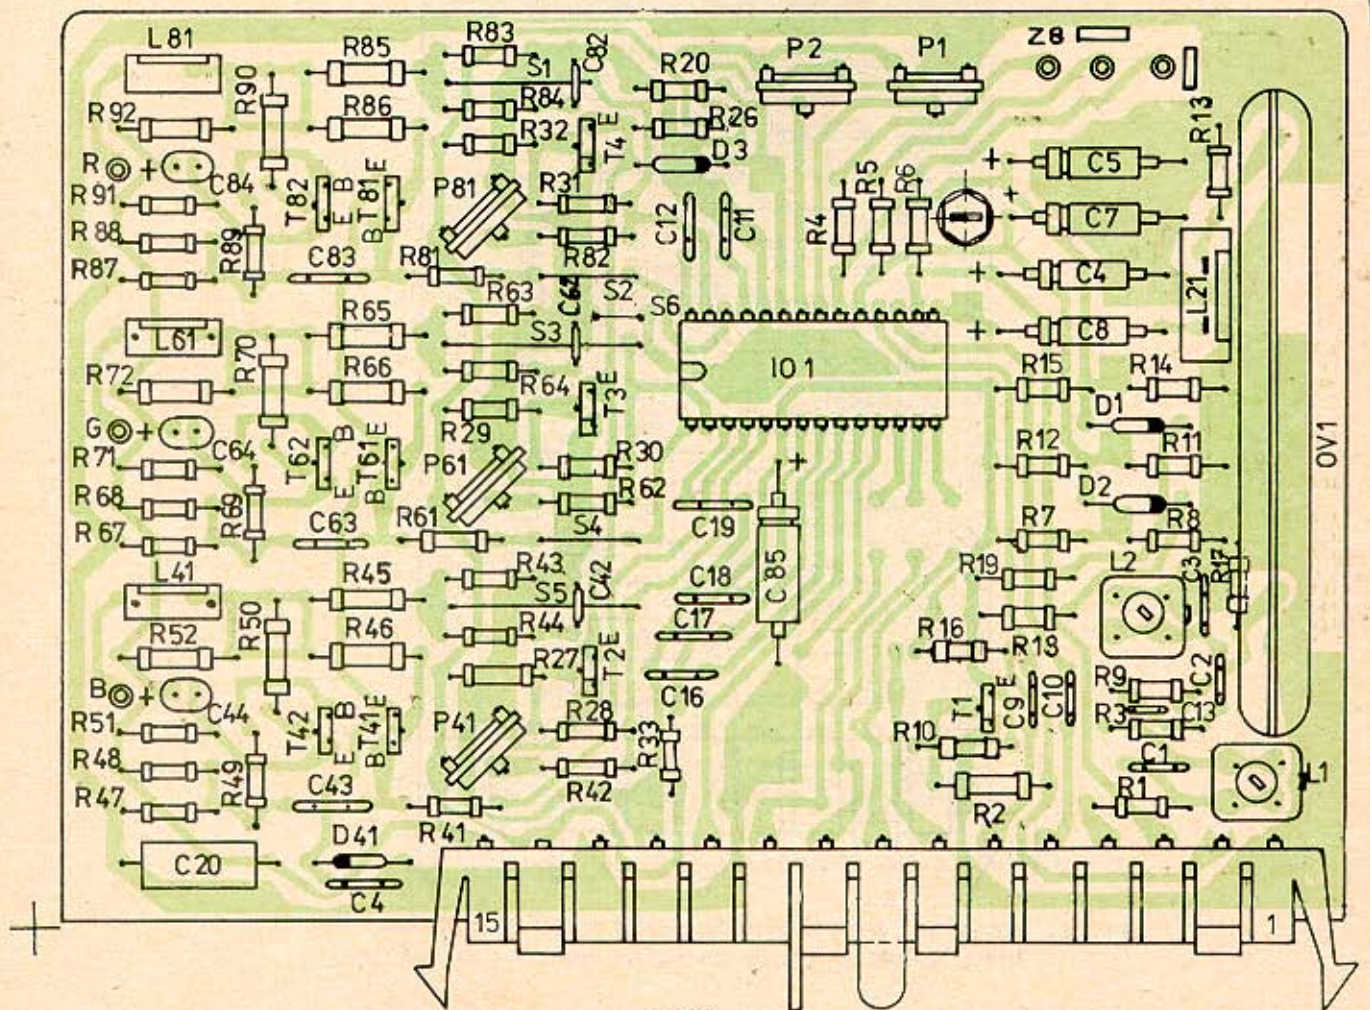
MODUL "P" 6PW 051 006 - POHLAD ZO STRANY SPOJOV
